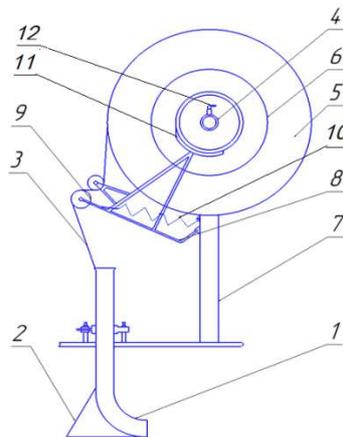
Укладчик капельной ленты с тормозным устройством: 1 - лентоукладочная труба; 2 - сошник; 3 - капельная лента; 4 - ось с подшипниковой опорой; 5 - катушка с лентой; 6 - прижимной диск; 7 - стойка; 8 - рычаг тормоза; 9 - ролик; 10 - пружина; 11 - колодка; 12 - держатель.
